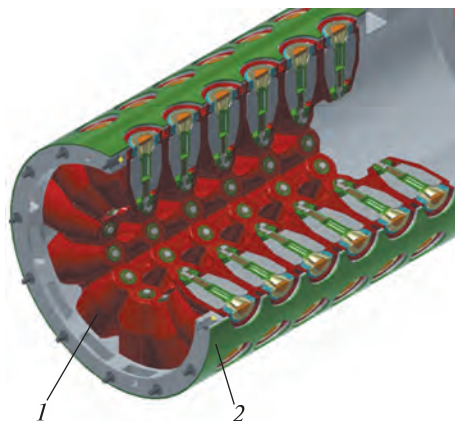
Конструктивная схема отсека ракеты: 1 — импульсный твердотопливный ракетный двигатель, 2 — отсек ракеты
